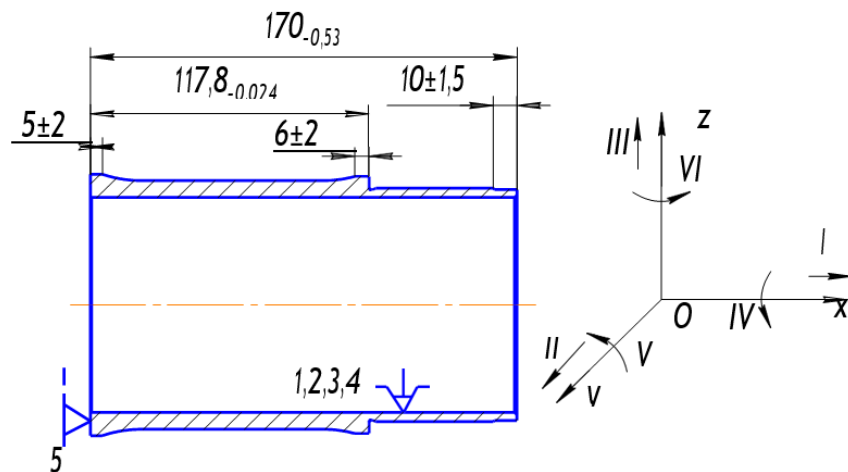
Схема базування і закріплення заготовки на операції 030
